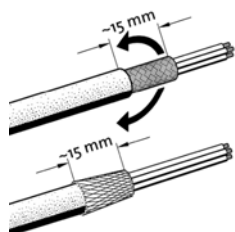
Montering af kabelskærme på EMC-kabelforskrutninger (SC...FC WM)
